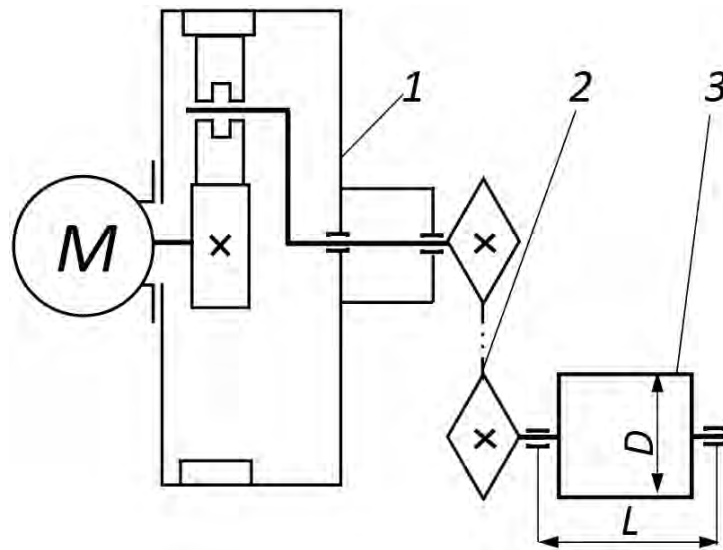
Схема привода сельскохозяйственной лебедки (вид сверху): 1 – мотор-редуктор (асинхронный электродвигатель с фланцевым исполнением закреплен на корпусе планетарного редуктора); 2 – цепная передача; 3 – приводной вал с барабаном
